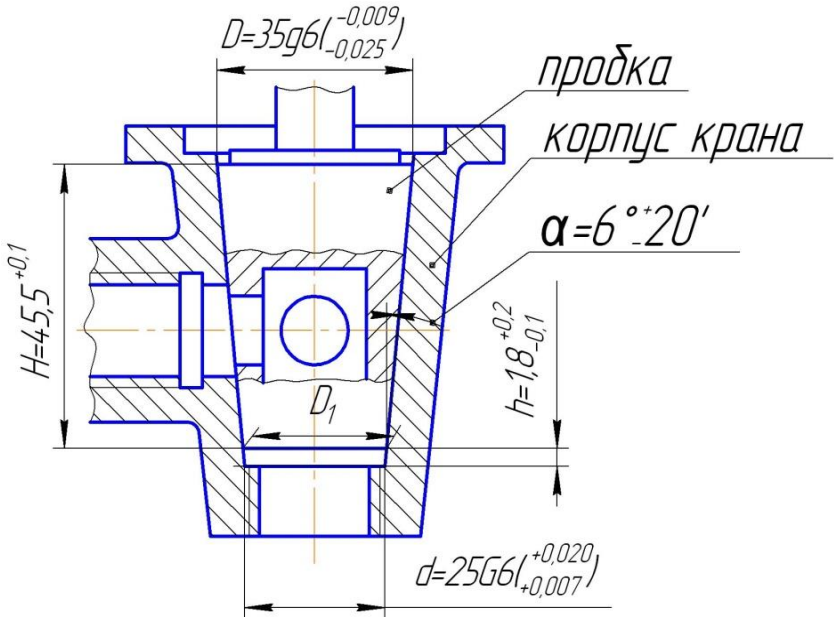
Схематизоване креслення вузла корпусу крана з пробкою
